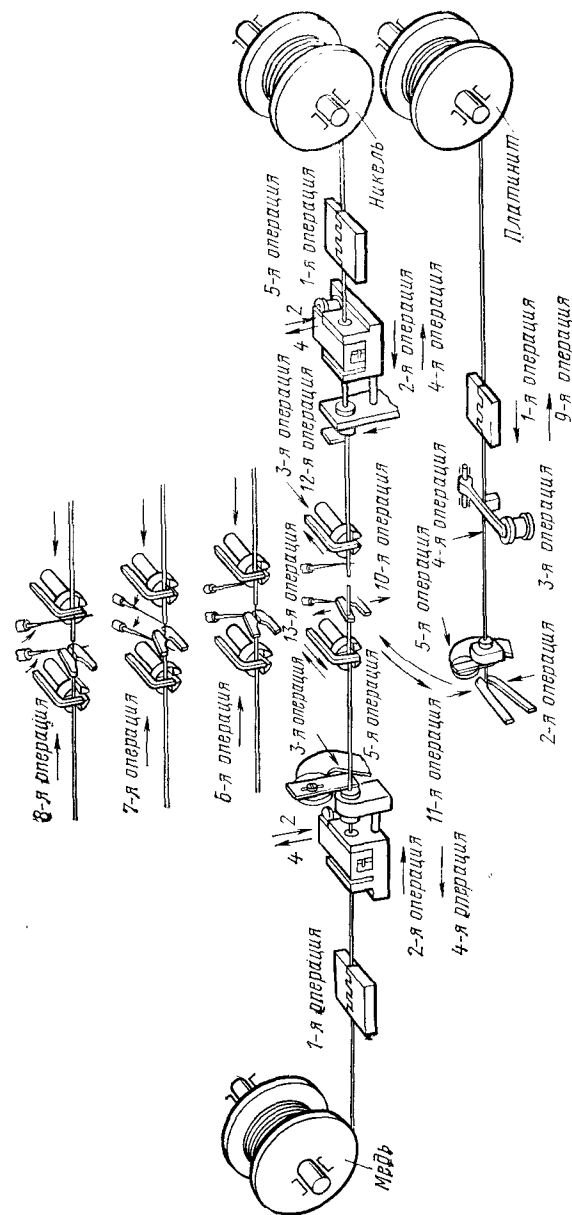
Технологический процесс газовой сварки вводов.
